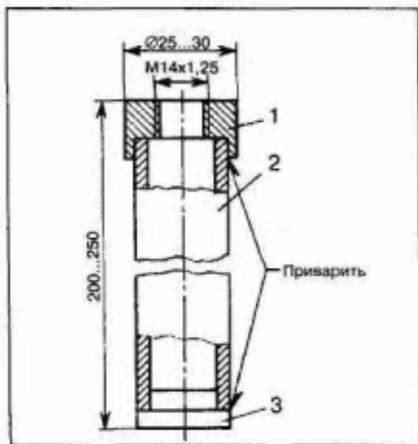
Приспособление для очистки свечей зажигания: 1 — втулка с резьбой под свечу; 2 — трубка; 3 — заглушка
